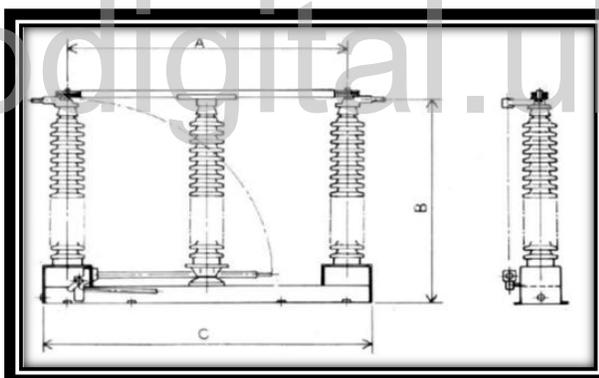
Seccionador de columna giratoria central y cuchillas de puesta a tierra hasta 220 kV. Fuente: [9]
